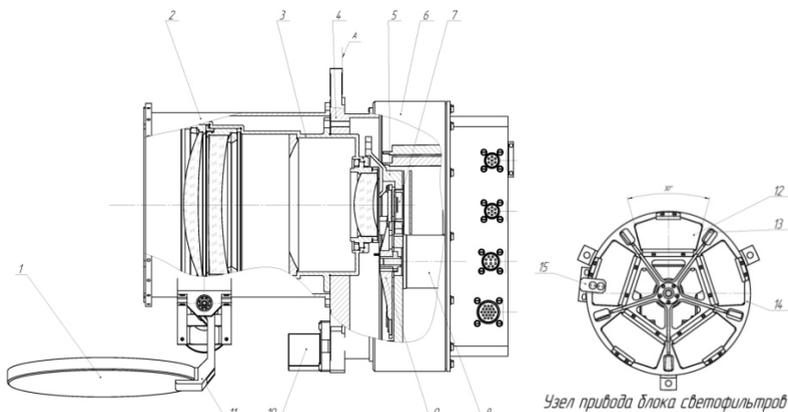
ИК-камера с болометрической матрицей: 1 – крышка; 2 – бленда; 3 – объектив; 4 – корпус; 5 – узел фотоприемника; 6 – кожух; 7 – микроболометрическая матрица; 8 – двигатель; 9 – узел привода блока светофильтров; 10 – контрольный элемент; 11 – поворотный кронштейн; 12 – светофильтры; 13 – щель; 14 – оправа; 15 – блок оптопар.
